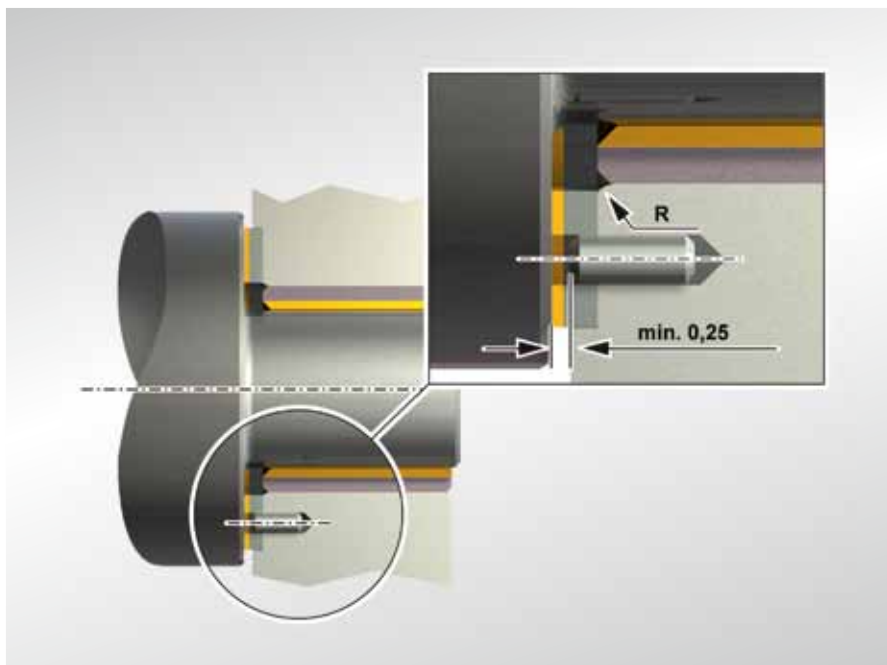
Befestigen einer Anlaufscheibe PAW in einer Ausnehmung des Gehäuses
